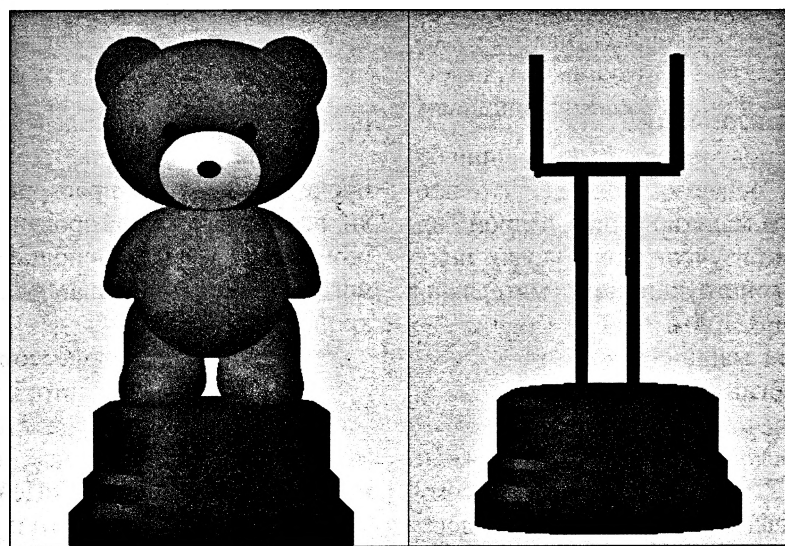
3D-модель в сборе и подставка с каркасом для сборки изделия
